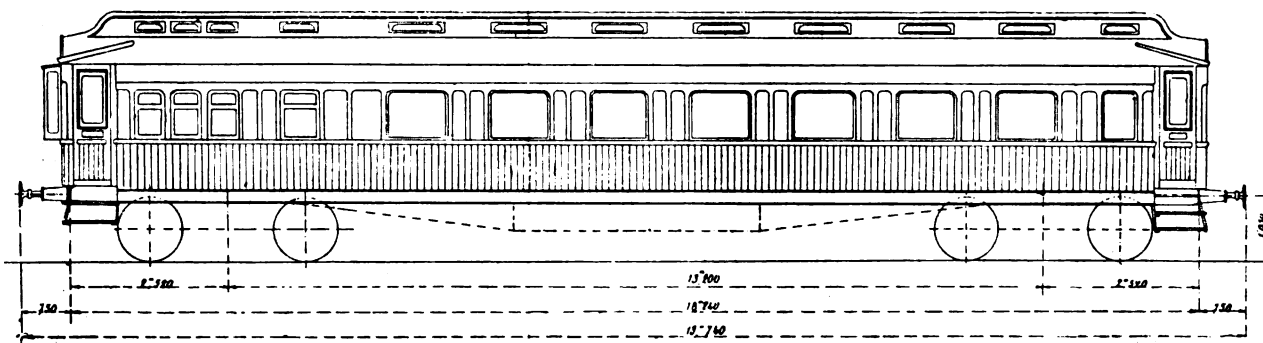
Prospetto della vettura restaurant n. 1650.
